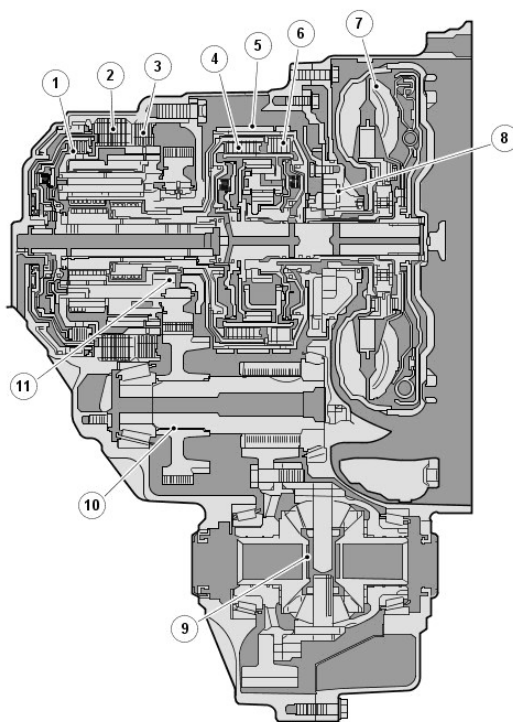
Автоматическая коробка передач AW F21 в разрезе
